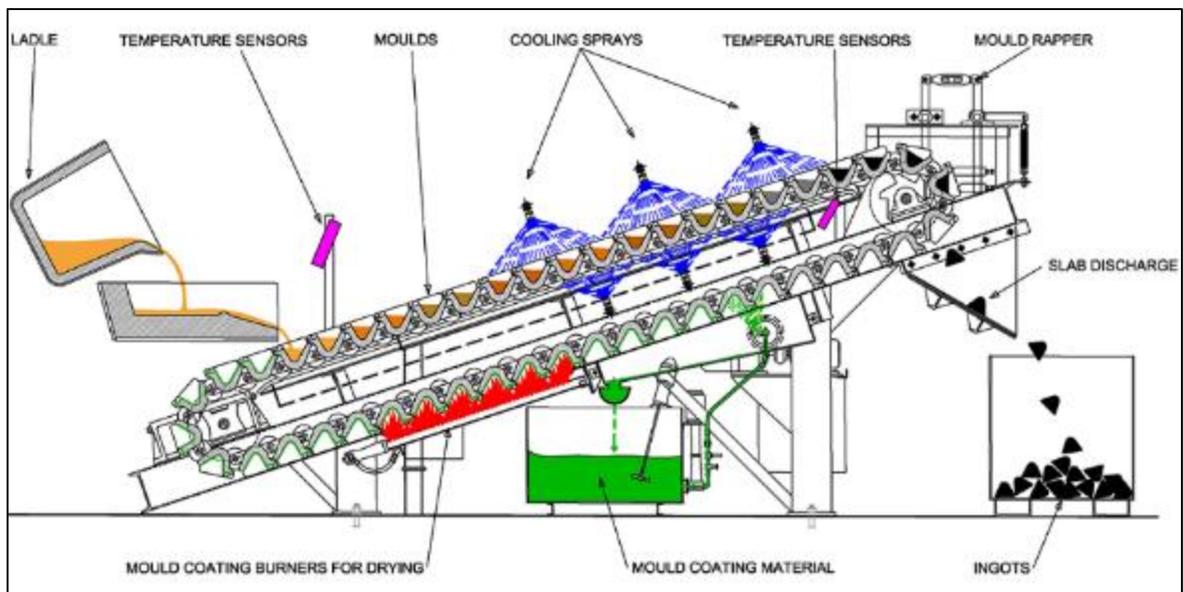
Máquina de colado de lingotes (Pig Casting Machine).
